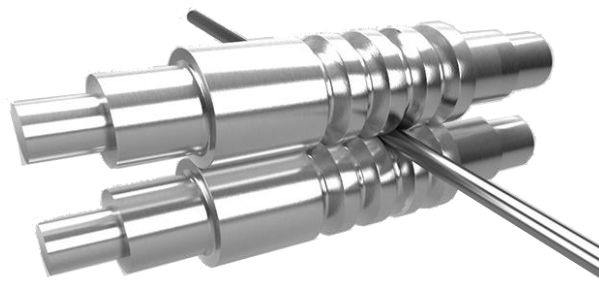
Комбинированные валки: 1 – гладкая бочка; 2 – калибр; 3 – прокатанный профиль
